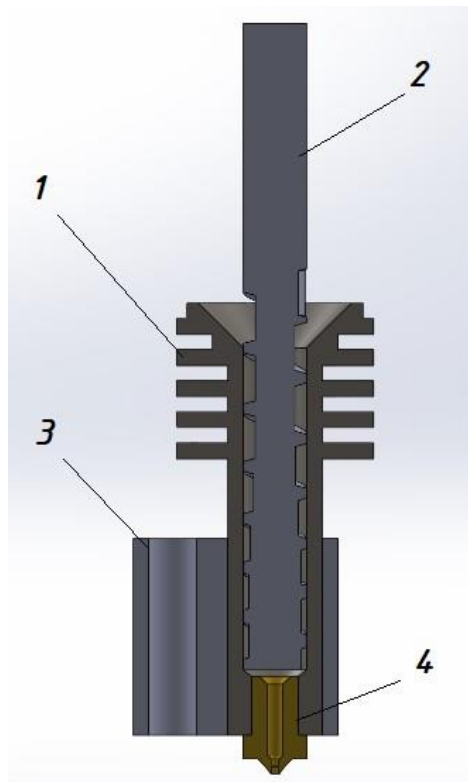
Модель екструдера в SolidWorks: 1 – матеріальний циліндр; 2 – шнек; 3 – нагрівальний елемент; 4 – сопло
